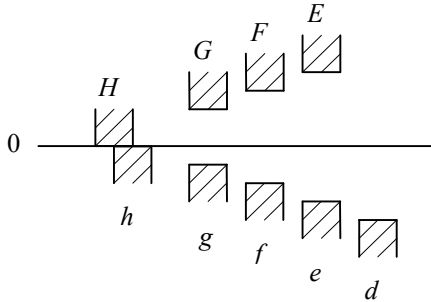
Схема розташування полів допусків різьб із посадками з зазорами.
